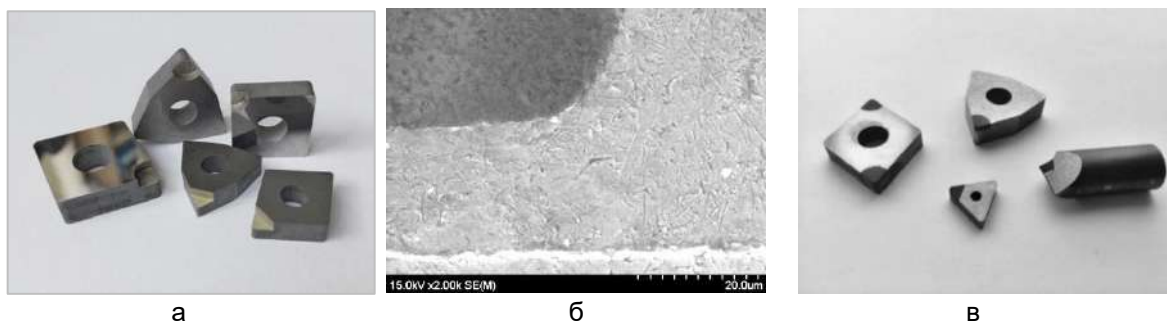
Внешний вид твердосплавных пластин различной конфигурации после электроэрозионной обработки (а); соединение твердосплавной режущей пластины и керамического режущего элемента, $\times 2000$ (б); режущие пластины после механической обработки (в)
